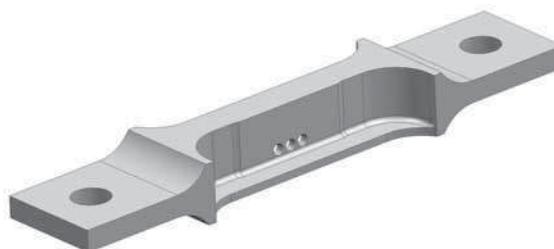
Конструктивно подобный образец стрингера с ОПТ
